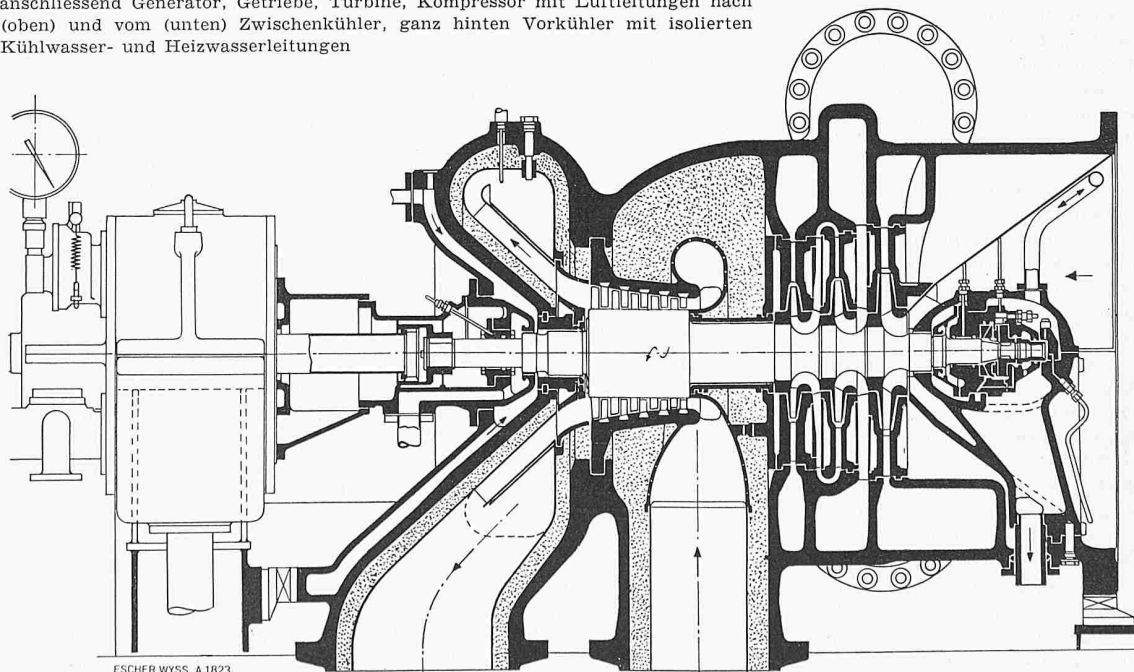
Längsschnitt durch die Maschinengruppe in TUCO-Bauweise
